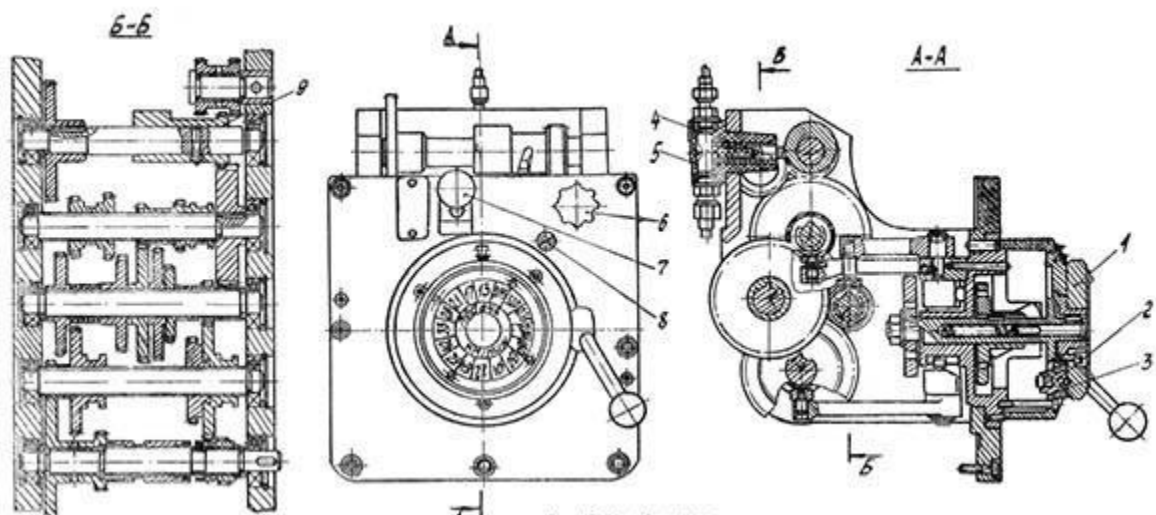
Коробка подач фрезерного верстата моделі 676
